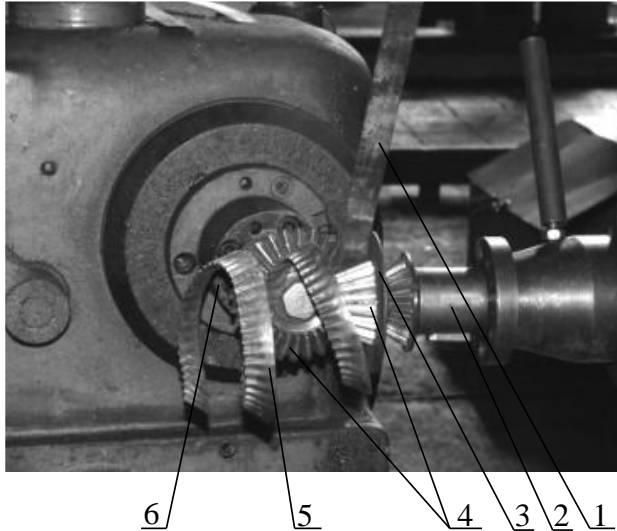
Формоутворення ГГЗ парою ортогональних формувальних інструментів ($\alpha=90^\circ$) на обкатному верстаті: 1 – смуга; 2 – ведучий шпиндель; 3 – упорне кільце; 4 – пара конічних зубчастих коліс; 5 – гвинтова гофрована заготовка; 6 – ведений шпиндель
